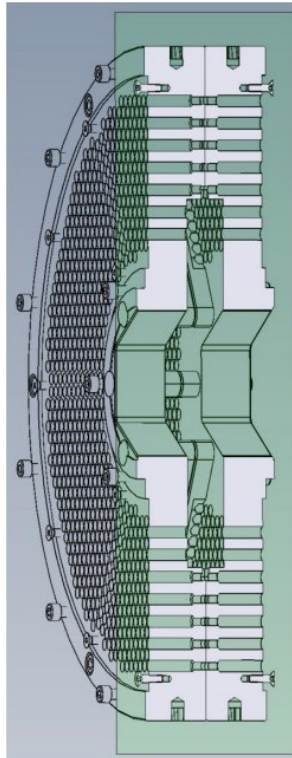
CAD-Schnittzeichnung durch die Filterträger
